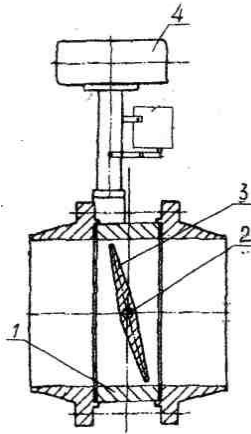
Дискава заслінка: 1 – корпус; 2 – вісь;
